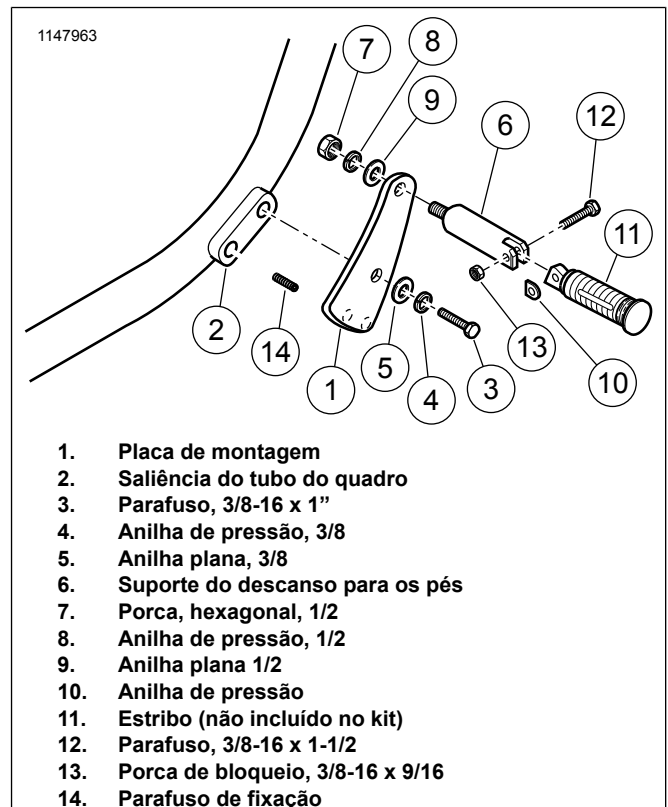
Instalação do estribo e do kit de montagem do estribo (lado direito do veículo)
